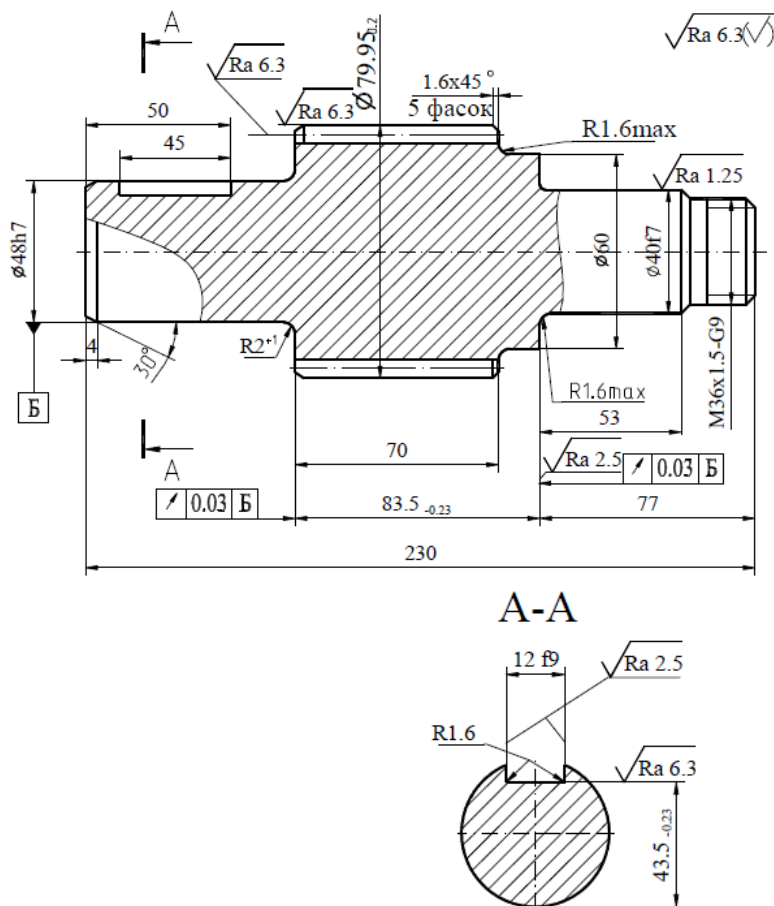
Креслення деталі «вал-шестерня»
